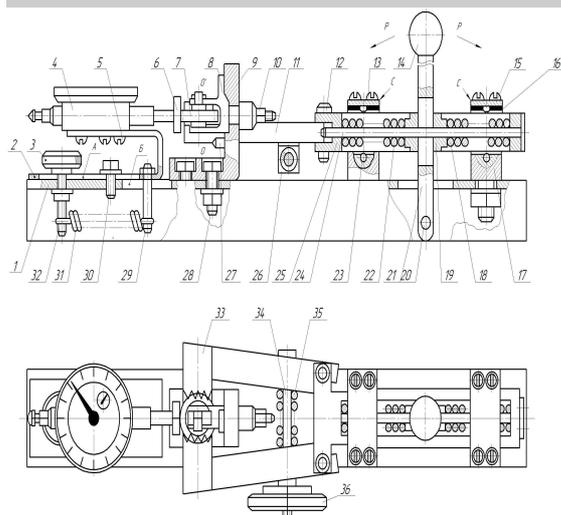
Устройство для замера радиального люфта узла промежуточной шестерни:
